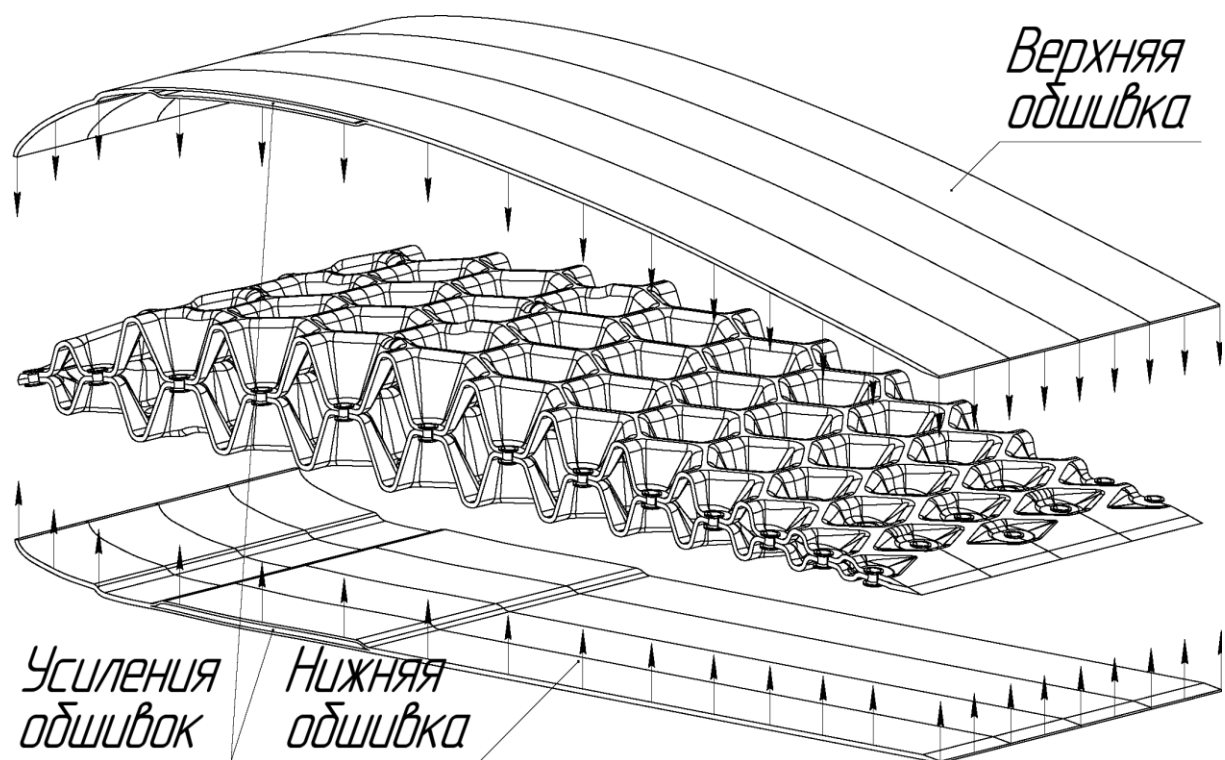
Процесс сборки многослойного дискретного заполнителя авиационной несущей поверхности заполнителя с несущими слоями (обшивкой)
